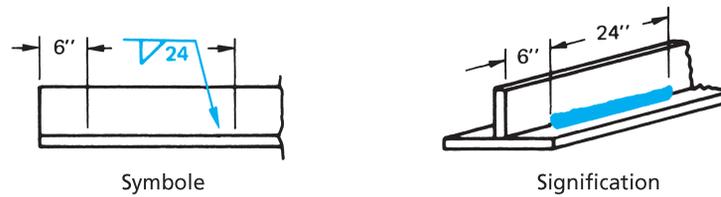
■ Longueur des soudures d'angle.
